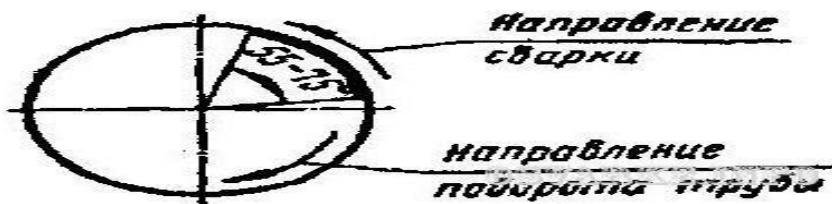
Схема сварки стыка труб малого диаметра
